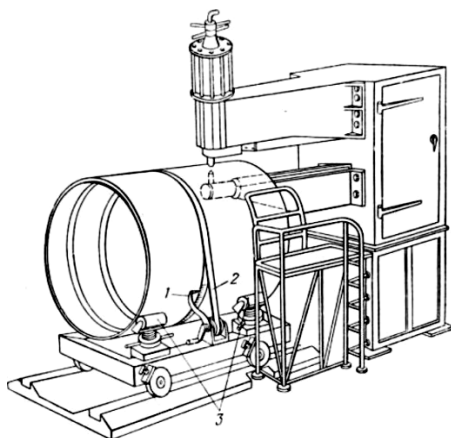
Приспособление для точечной сварки крупногабаритных изделий:
